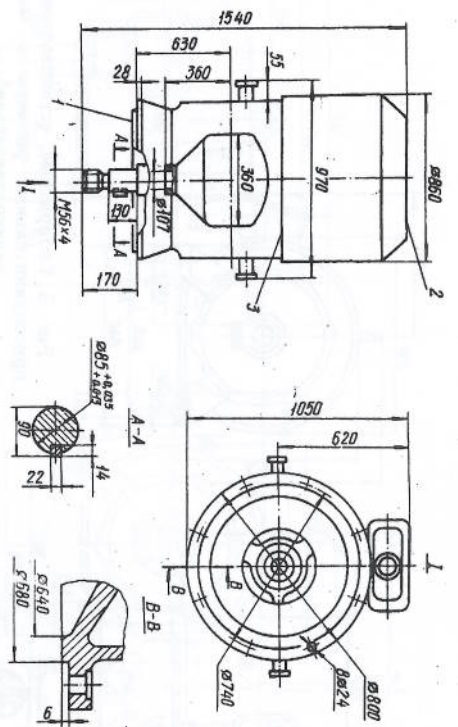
Габаритные, установочные, присоединительные размеры электродвигателей АОЗ-400М-6У2 IM3011, АОЗ-400М-6Т2 IM3011 и АОЗ-400М-4У2 IM3011. Масса электродвигателей 2200 кг
